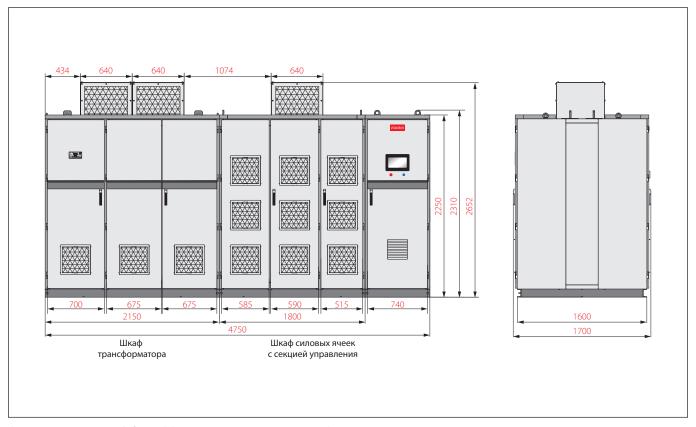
Корпуса DC03 и DD03 на напряжение 10 и 11 кВ
